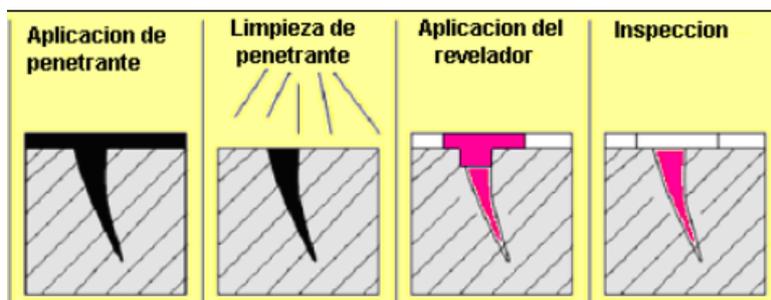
Pasos a seguir para realizar prueba de Líquidos Penetrantes.
